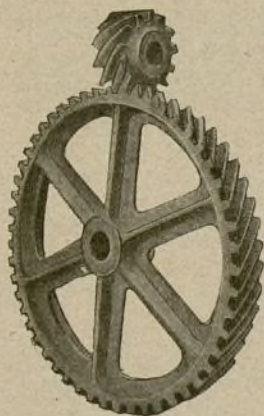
Cuplo de engranajes helicoidales (dentadura a la izquierda y ejes a 90°).
